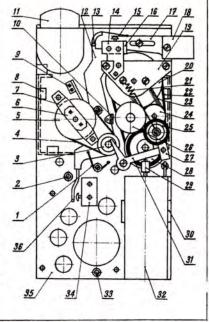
Лентопротяжный механизм в сборе (вид снизу): 1— возвратная пружина рычага 12; 2, 33— резьбовые стойки крепления основной печатной платы; 3 — ролик привода подающего узла; 4, 22 — пассики резиновые; 5 шкив-подкассетник подающего узла; 6 — втулка; 7 — кронштейн; 8 — фи-ксатор кассеты; 9, 10 — подтормаживающие устройства подающего и приемного узла соответственно; 11микроамперметр М476; 12 — рычаг обратной перемотки; 13- штифт; 14планка; 15 — пружина; 16,34— микропереключатели; 17 — рычаг переключателя рода работ; 18 — ручка управления; 19 — пластина; 20 — маховик ведущего вала; 21— пружина; 23— пассик пружинный; 24— шкив промежуточного узла; 25 — ролик обрези-ненный; 26 — диск приемного узла; 27,31 — рычаг ролика 25; 28 — шкив; 29 — насадка; 30 — скоба электродви-32 — электродвигатель гателя; гране; 35— шасси ЛПМ, Ст. 20 толщиной 1,5 мм; 36— пружина.
